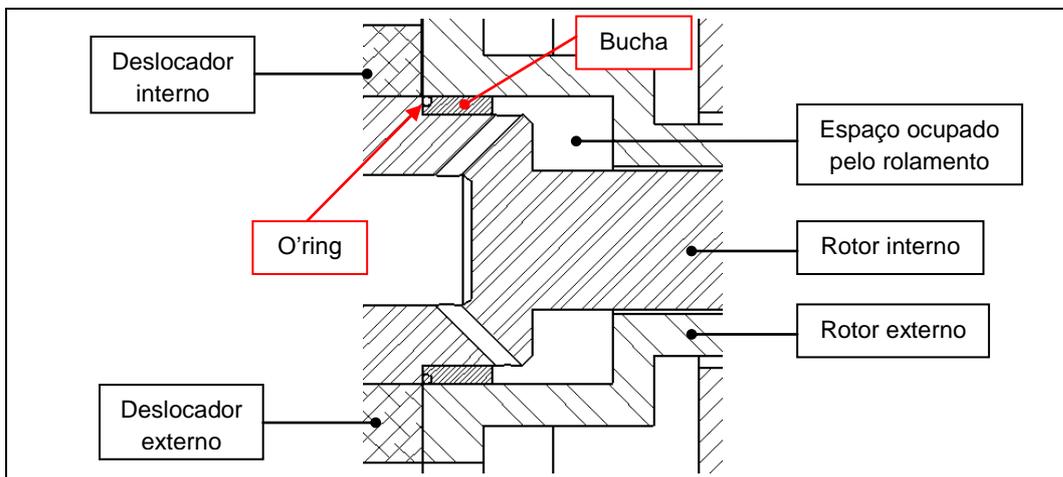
Detalhe de montagem da bucha do rotor interno.
